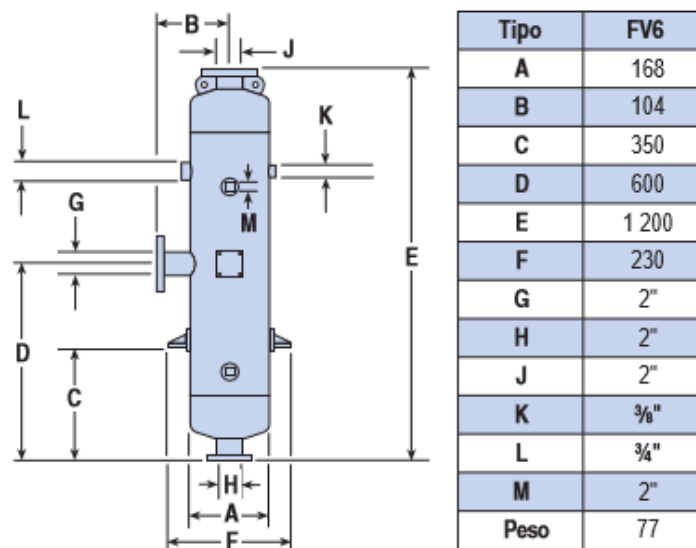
16: Dimensiones del tanque de vaporizado FV6/M310 “flash” [17].
